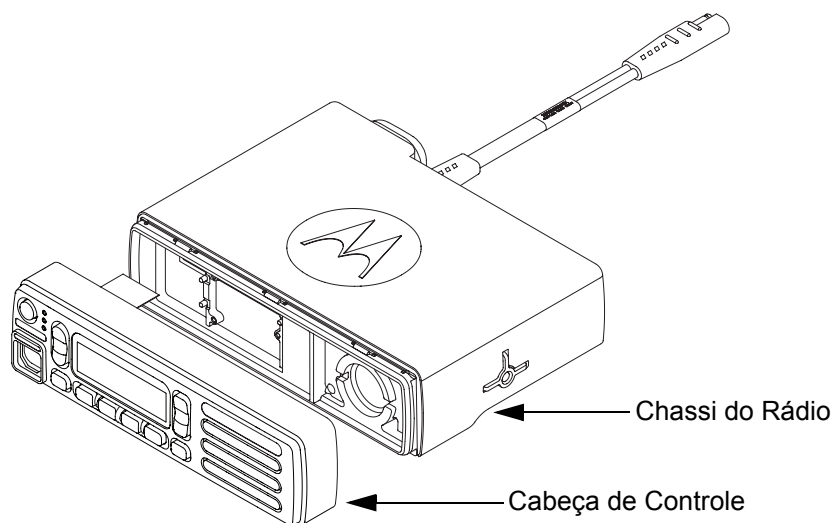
Montagem da Cabeça de Controle no Chassi
